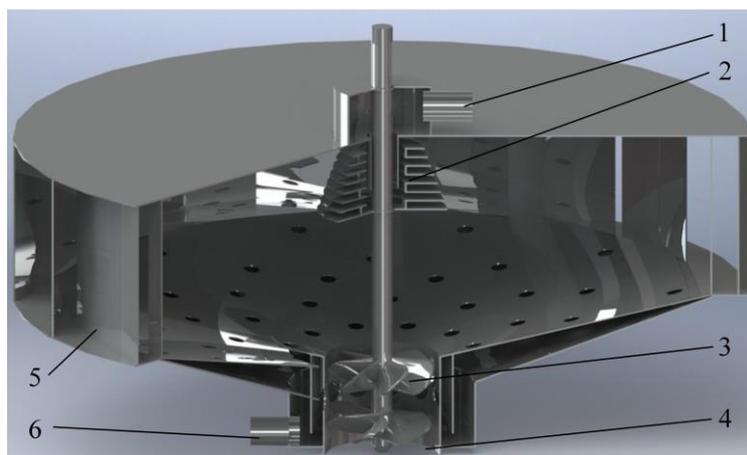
Внешний вид вихревой камеры с дисковым распылителем [1]: 1 – патрубок для входа оборотной воды; 2 – дисковый распылитель; 3 – лопасти; 4 – патрубок для выхода воздуха; 5 – тангенциально-лопаточный завихритель; 6 – патрубок для отвода охлажденной воды
